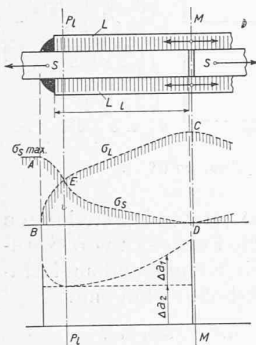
Stab mit Fuge; Flacheisen in Stirn- und Flankennähten angeschweisst.
